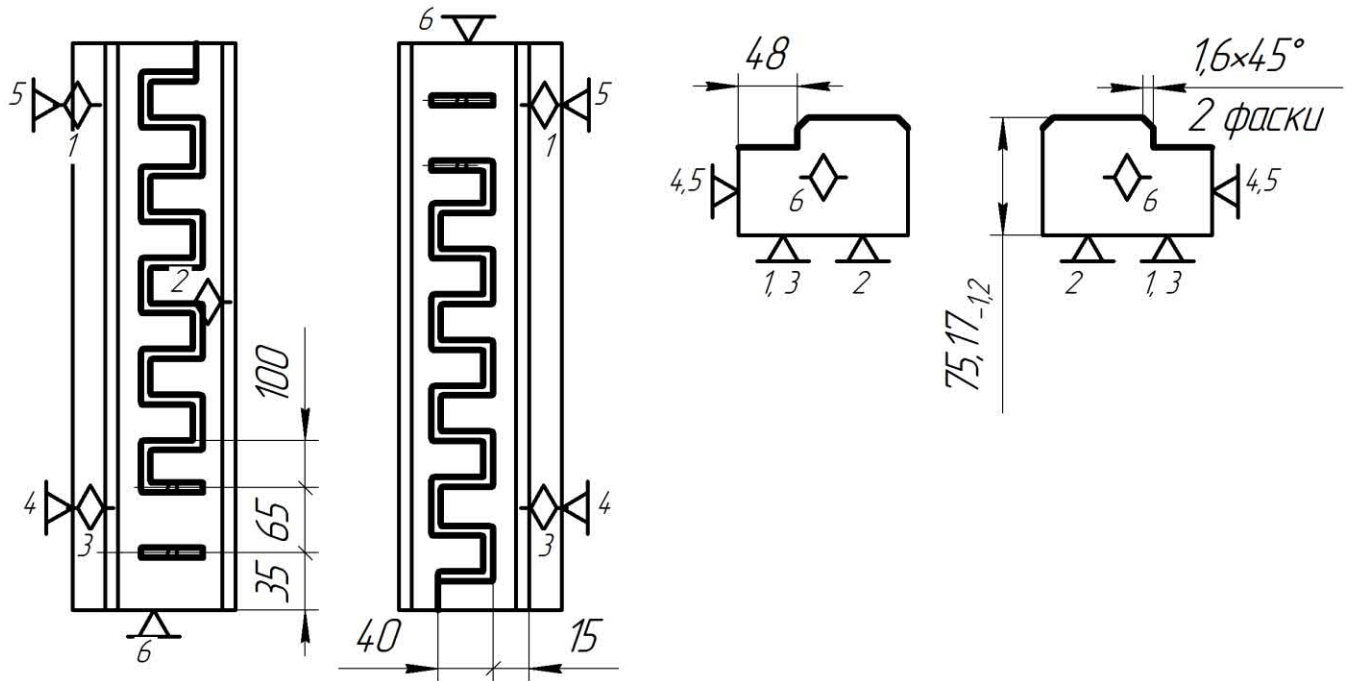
Ескіз обробки і схема базування на операцію 025
